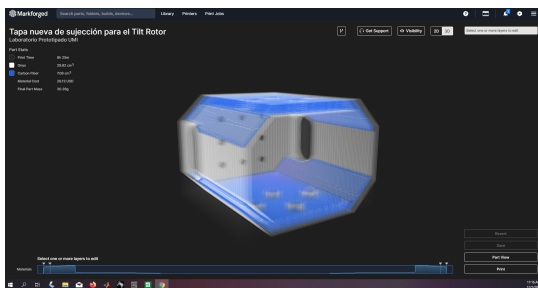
Refuerzo fabricado en Onix mediante la técnica de FDM.
